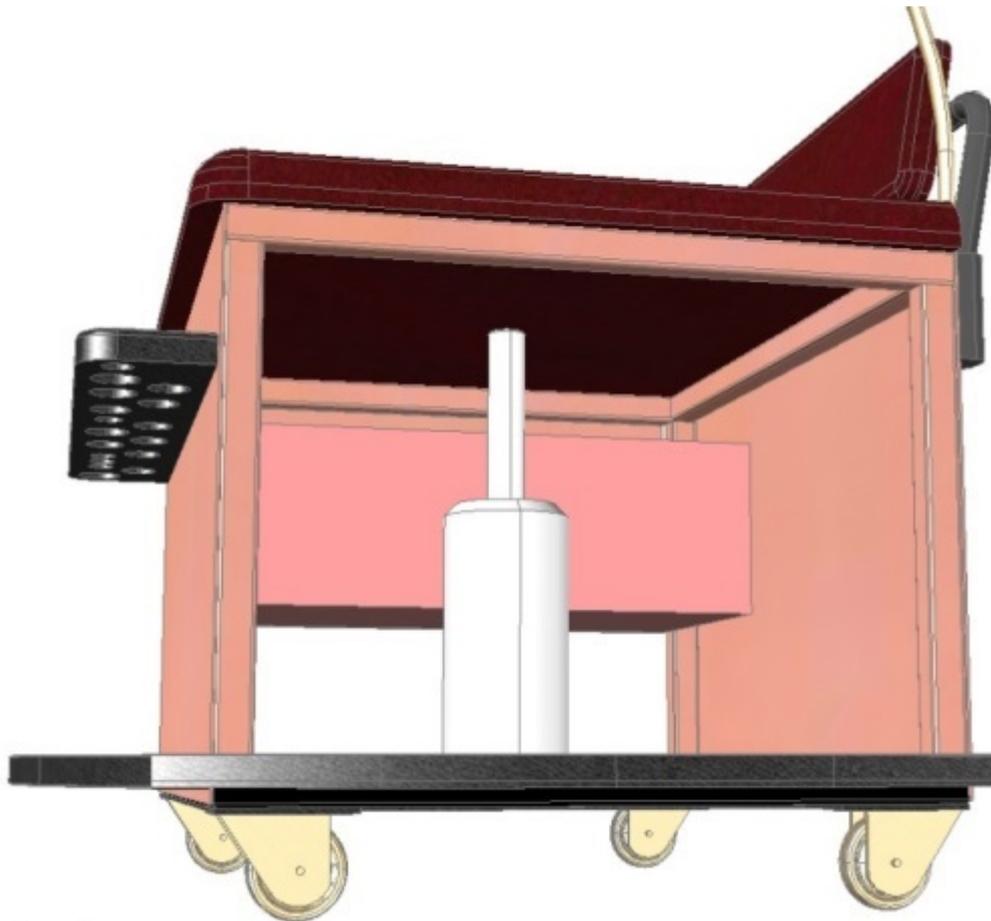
Механизм регулировки высоты подъема ремонтного стула
